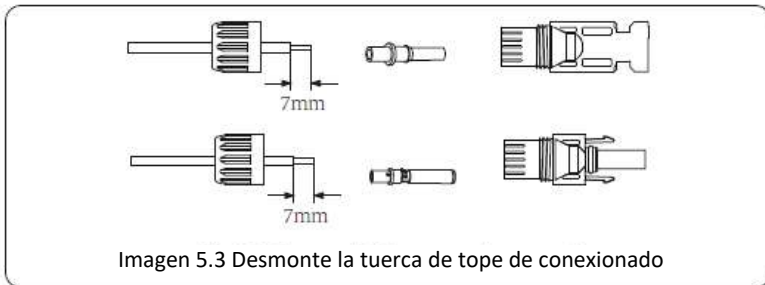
Desmonte la tuerca de tope de conexionado
